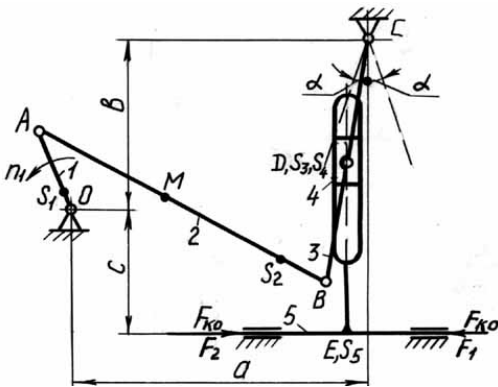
Кінематична схема механізму коливального конвеєра
